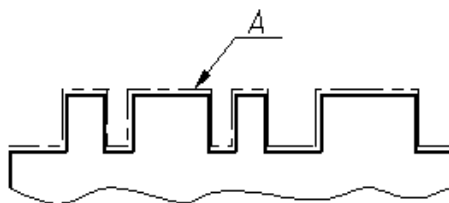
Пример обозначения поверхности сложной формы, имеющей одинаковую шероховатость
